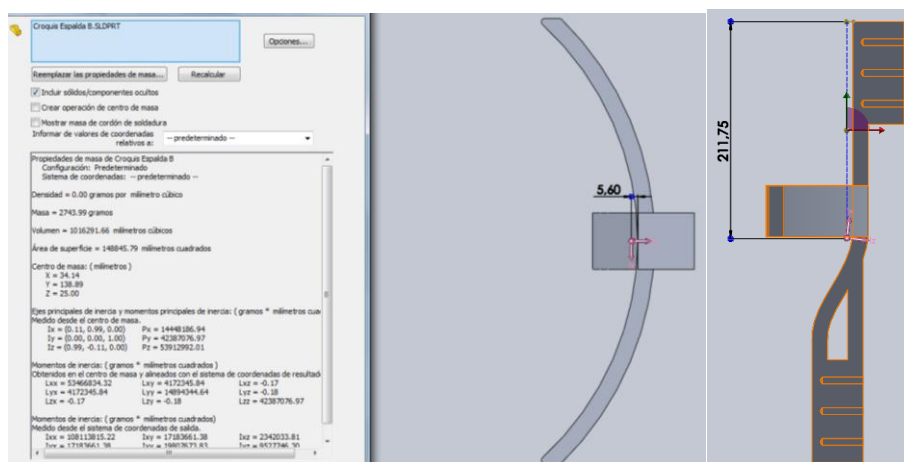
Centro de masa del ensamblaje de sección B - espalda
